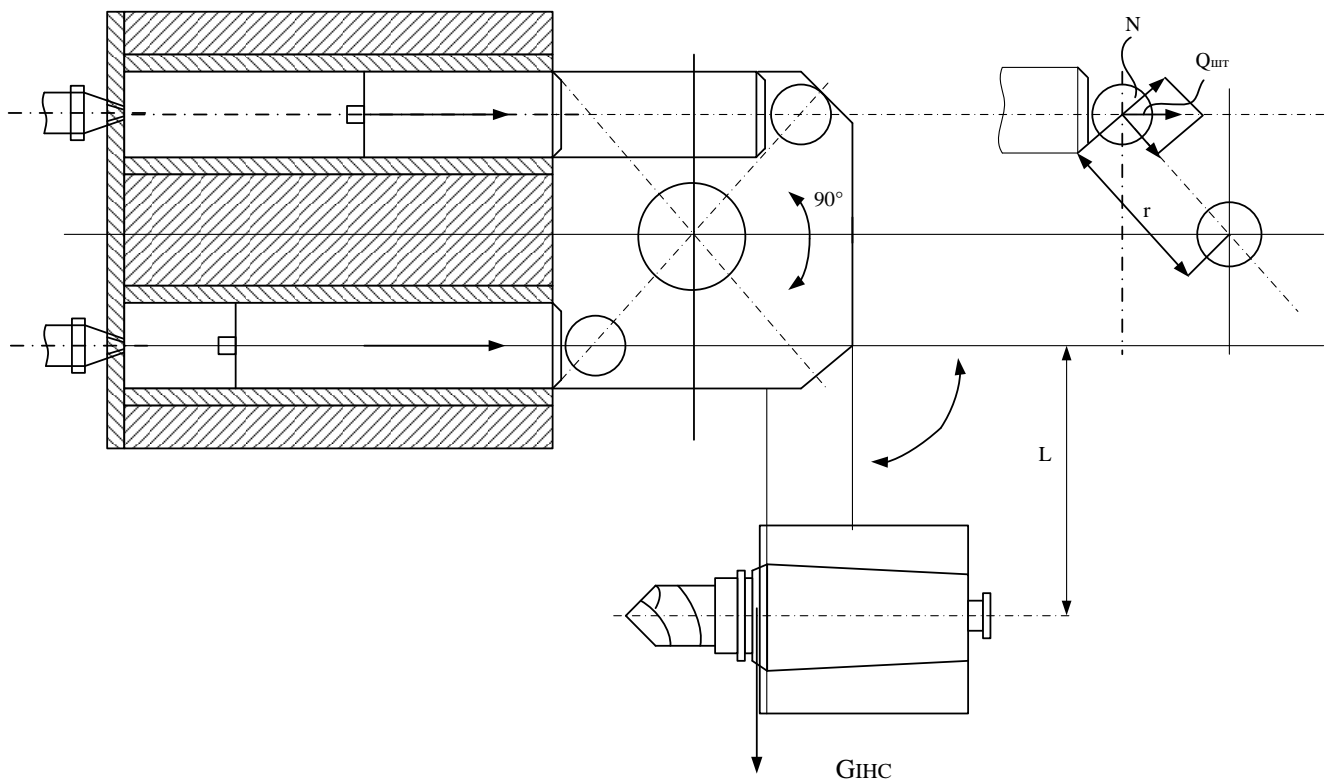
Розрахункова схема приводу повороту лапки кантувача
